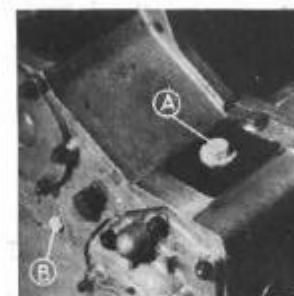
Tapones de llenado y nivel de la caja reductora.
